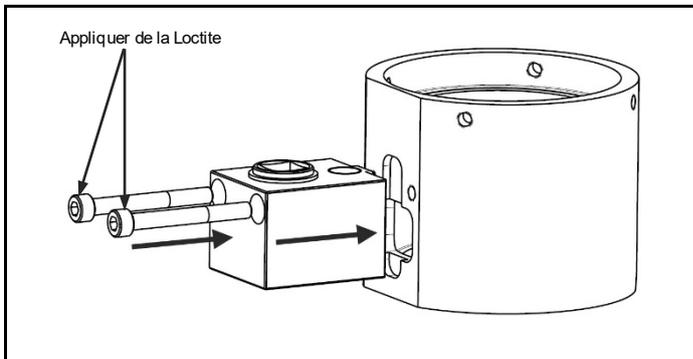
Appliquer de la Loctite sur les vis creuses; fixer la boîte d'engrenages assemblée sur le pont
